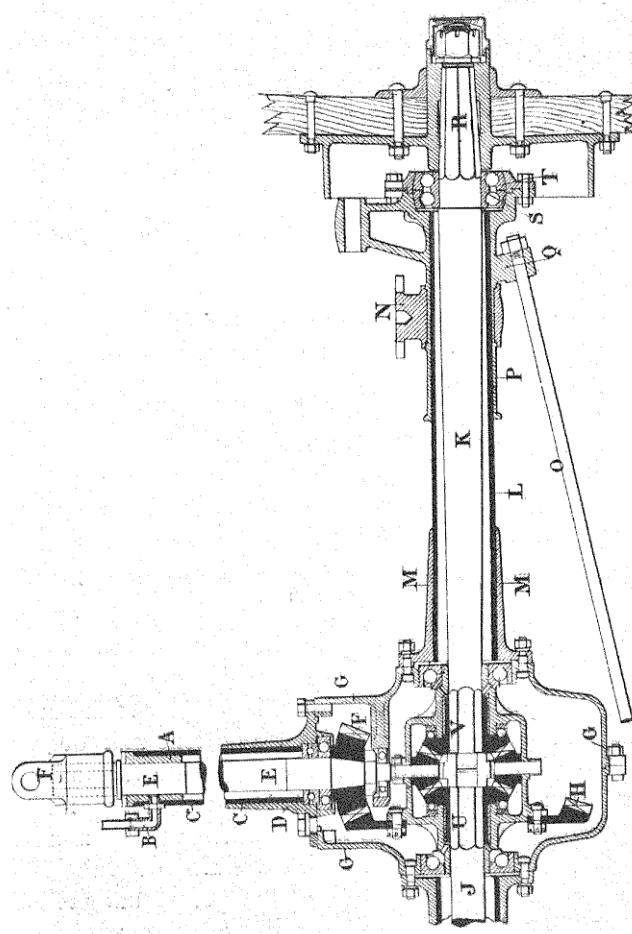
Essieu arrière moteur à patins oscillants, et roues en porte-à-faux.
